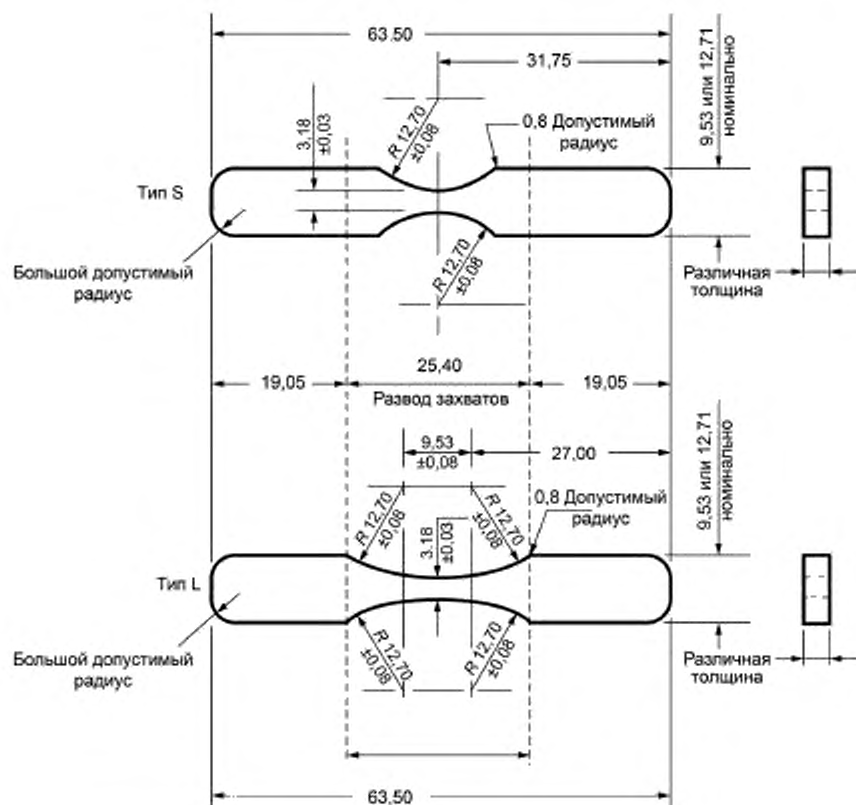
Размеры пресс-формы образцов типов S и L для ударного растяжения (в миллиметрах)
